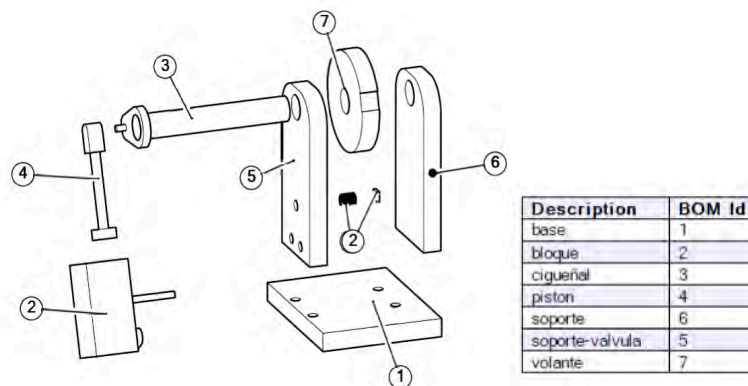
Componentes principales del motor de cilindro oscilante.
